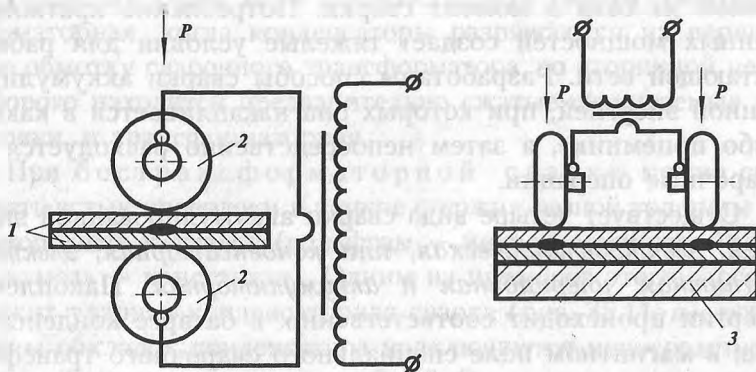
Принципиальная схема шовной сварки: 1 — заготовки; 2 — электроды; 3 — медная подкладка
